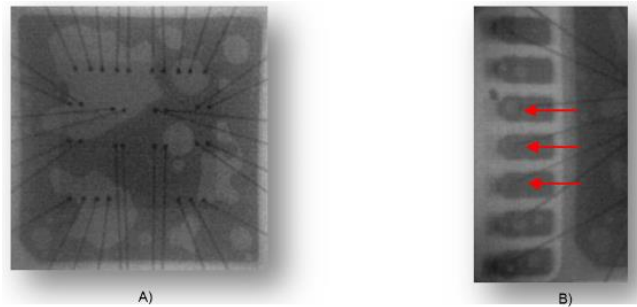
Imagen de Rayos-X mostrando A) Formación excesiva de huecos causando insuficiencia de soldadura en la huella térmica y B) Conexiones de soldadura abiertas debidas a exceso de soldadura.
